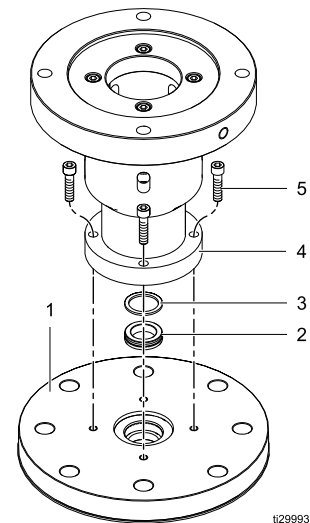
Austausch der Wellendichtung für die Flansch-/Schnellspann-Montage
